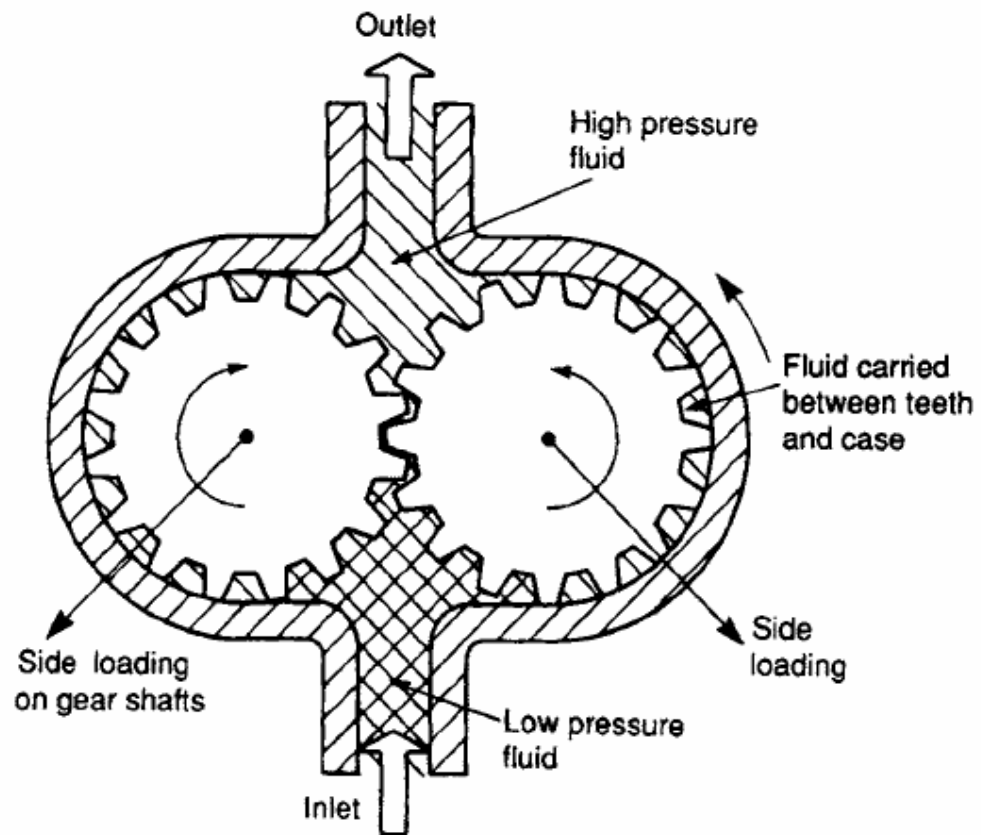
Coupe d'une pompe a engrenage [6].
